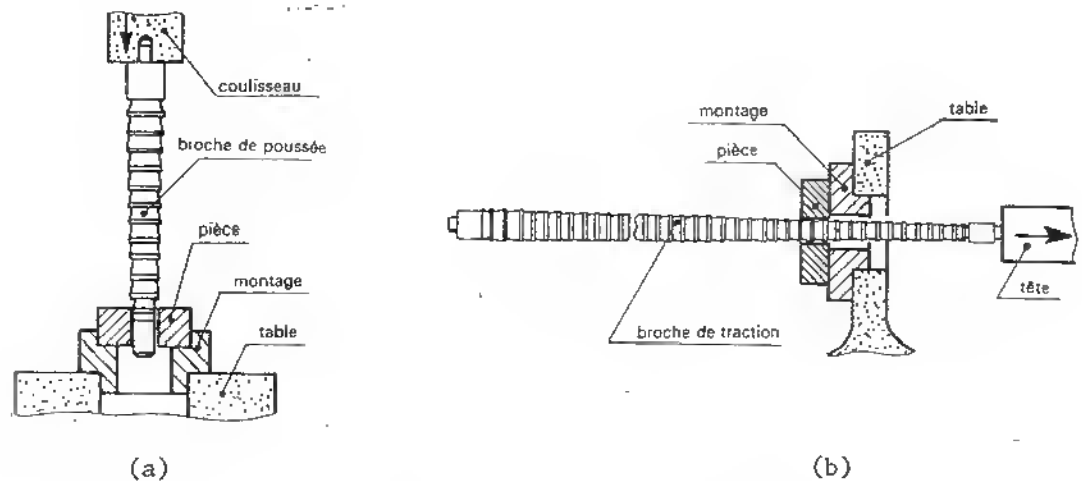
Principe des machines à brocher. La broche est (a) poussée ou (b) tirée à travers la pièce.
